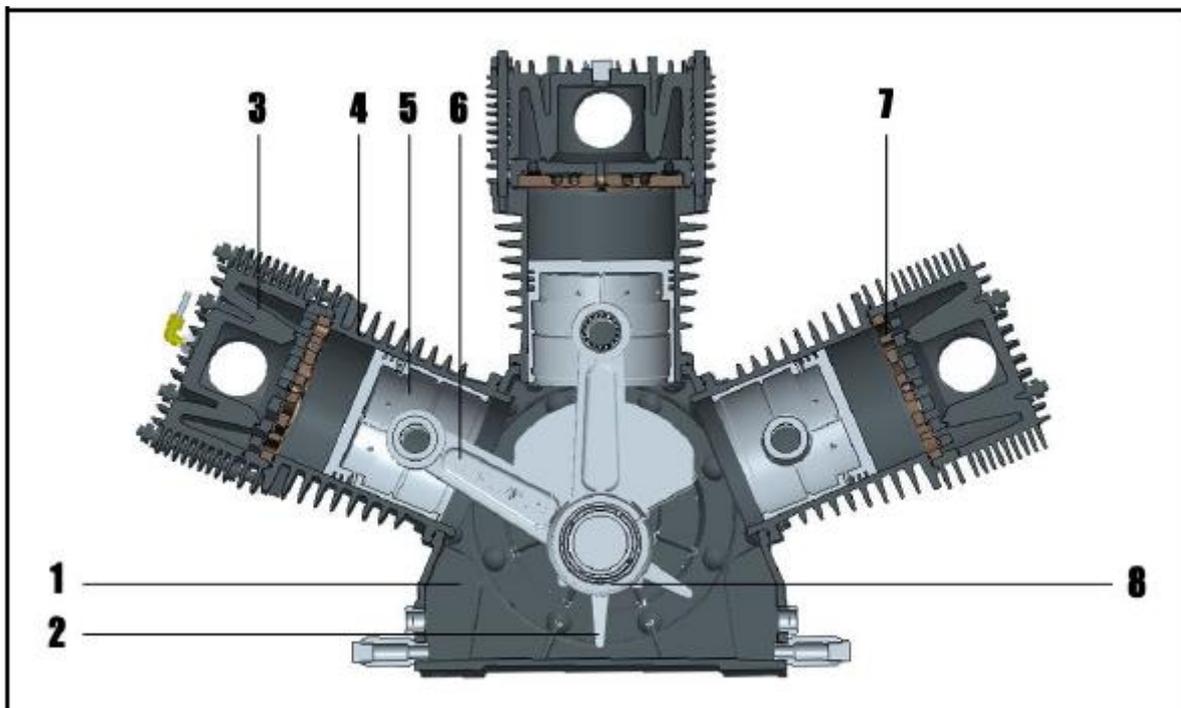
Общий вид поршневых компрессоров низкого давления
